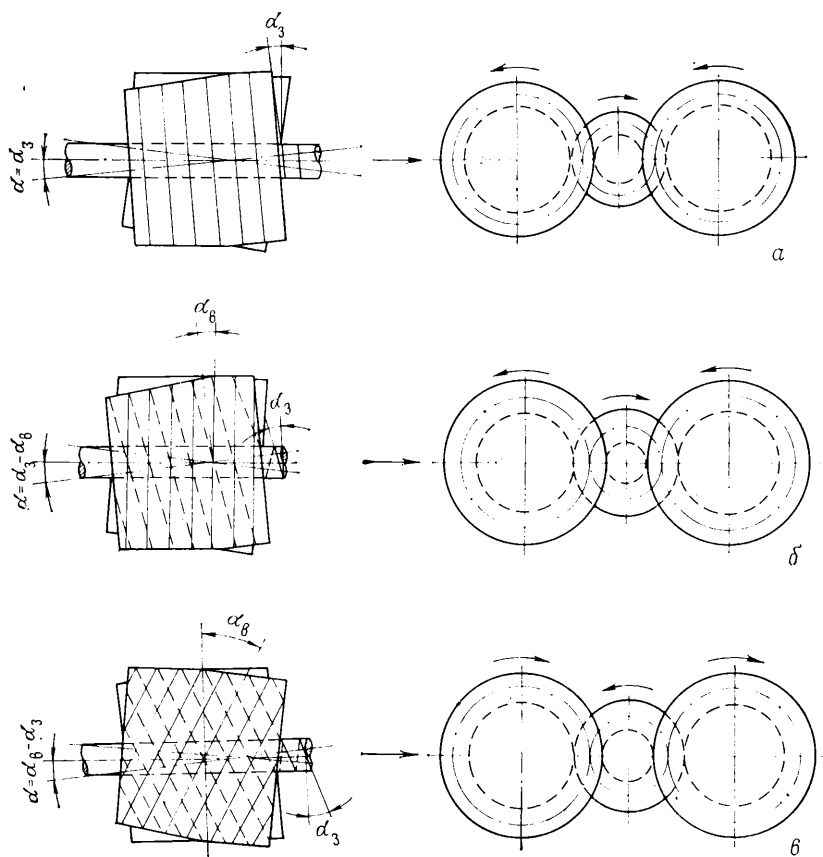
Схемы прокатки в валках с кольцевыми и винтовыми калибрами
